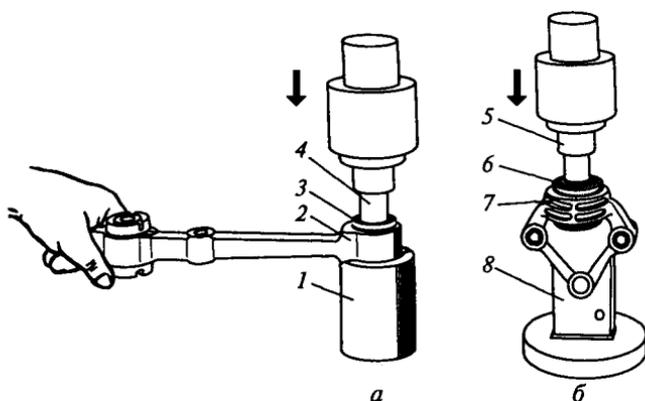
Выпрессовка резинометаллических шарниров из рычага подвески (а) и кронштейна крепления растяжки (б):
